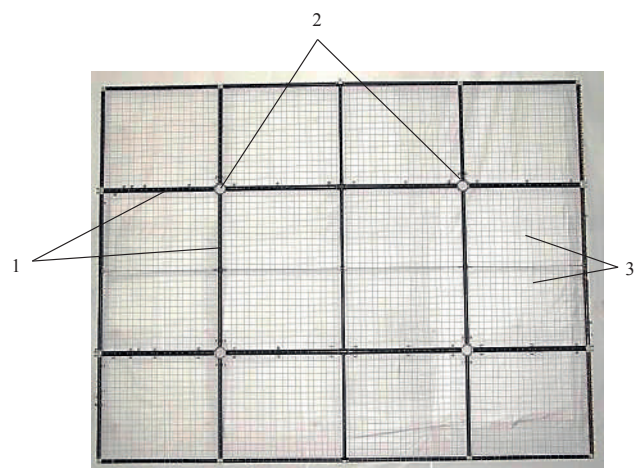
Конструкция каркаса солнечной батареи: 1 – углепластиковая труба круглого сечения; 2 – фитинг; 3 – струна
